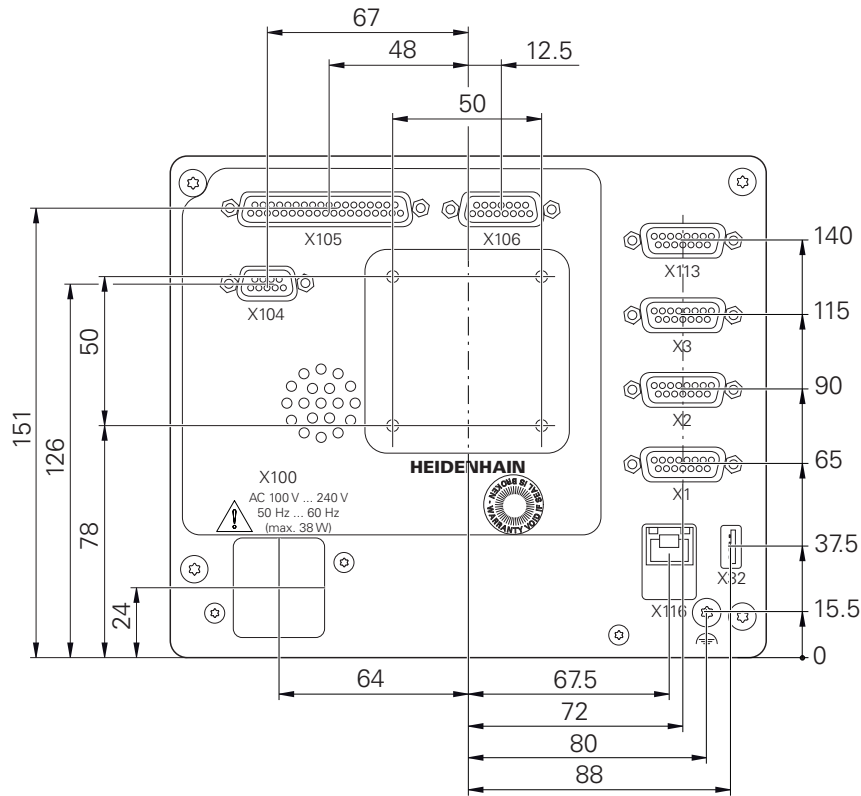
Dimensioner för baksidan på enheten med ID 1089179-xx
